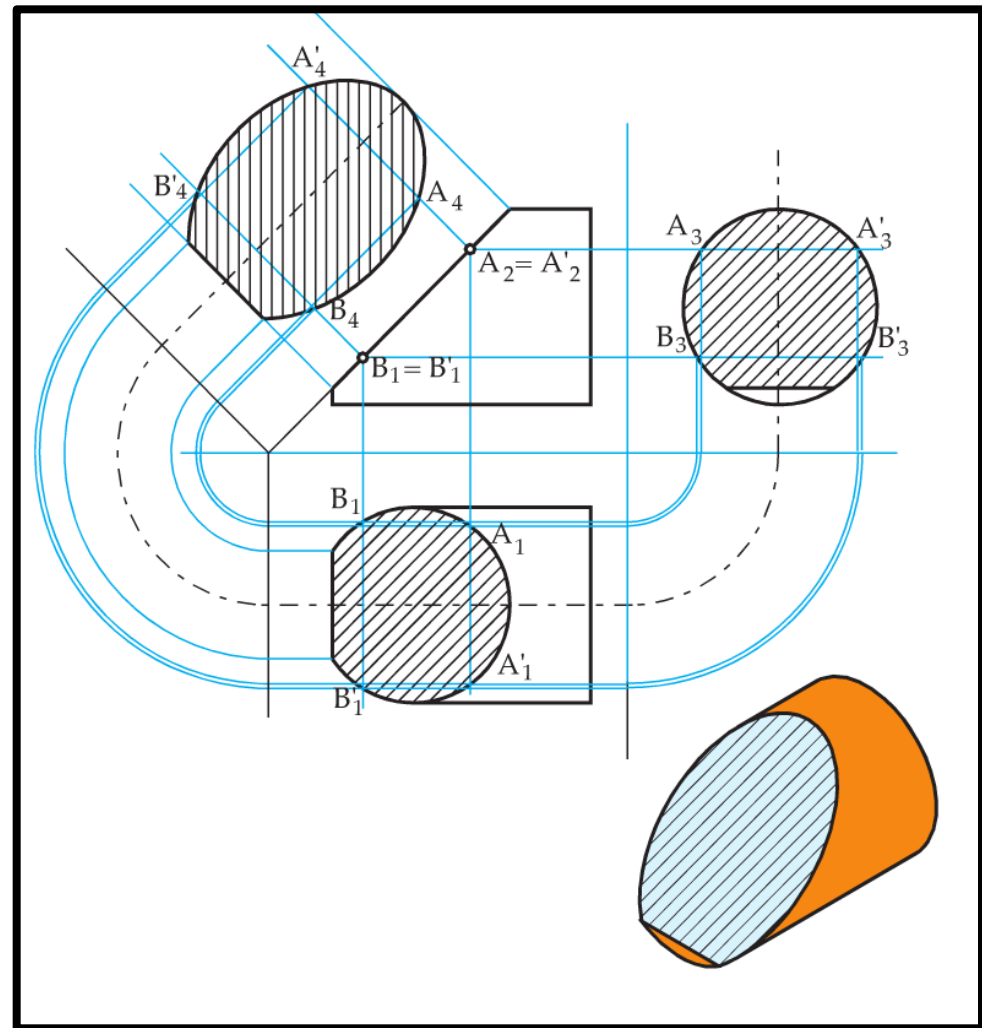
Sezione di un cilindro con un piano inclinato rispetto all'asse.
